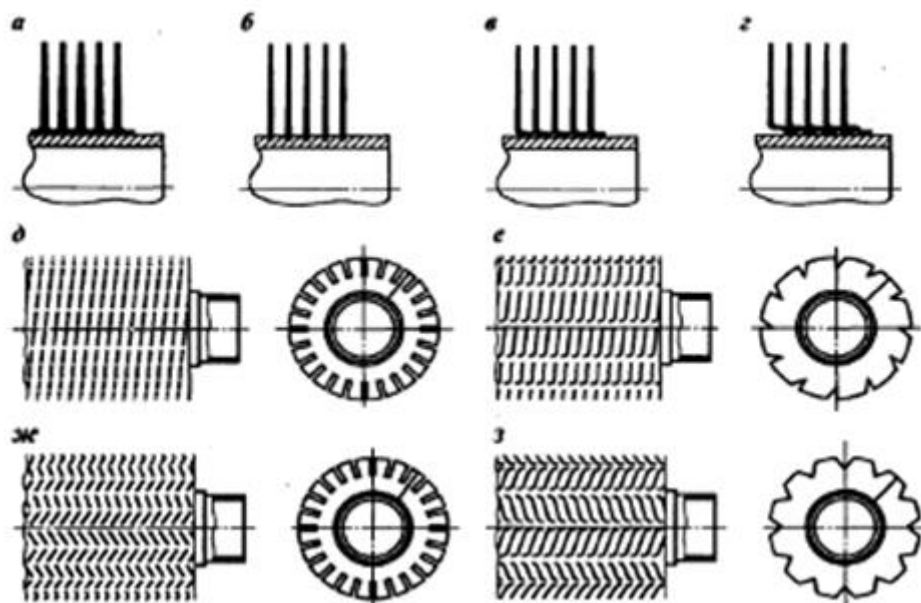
Способы крепления и виды оребрения на трубах.
